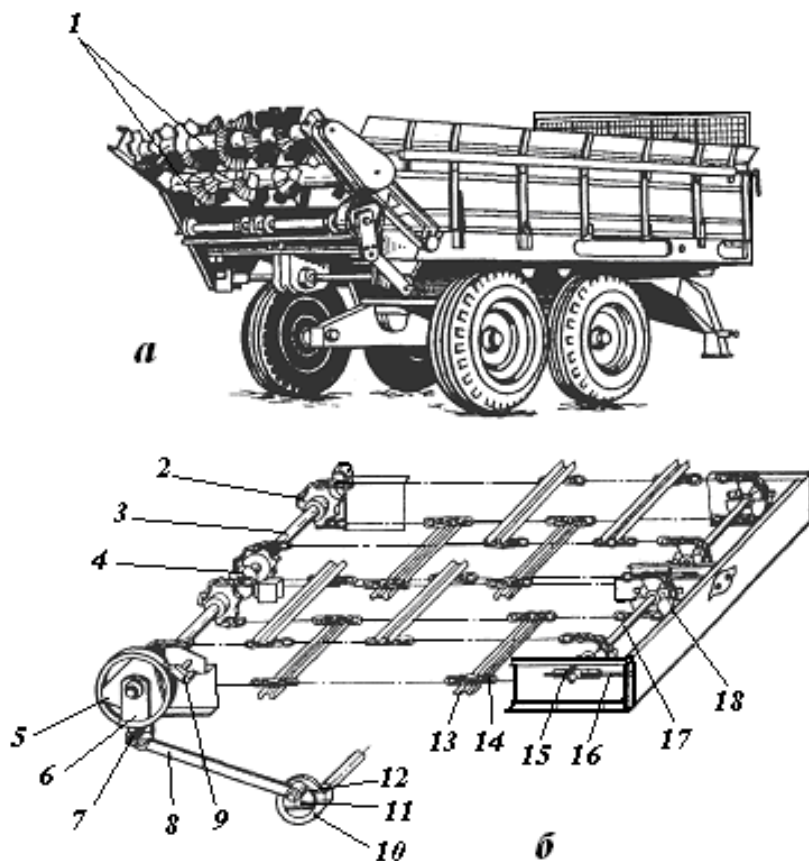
Розкидач органічних добрив РОУ-6: а - загальний вигляд; б - транспортер: 1 - розкидальний пристрій; 2 - ведуча зірочка; 3 - ведучий вал; 4 - опорний підшипник; 5 - храпове колесо; 6 - шоки; 7 - ведуча собачка; 8 - тяга; 9 - запобіжна собачка; 10 - корпус кривошипа; 11 - куліса; 12 - диск кривошипа; 13 - скребок; 14 - ланцюг; 15 - гайка; 16 - натяжний болт; 17 - ведений вал; 18 - ролик
